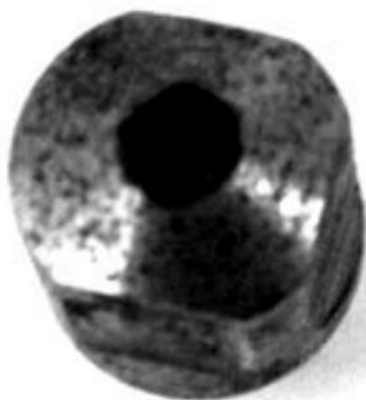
Фото інструменту зі зруйнованою робочою вставкою.
